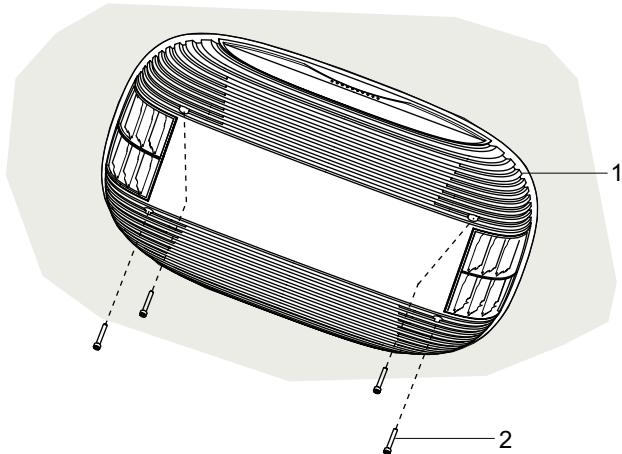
Fijación del conjunto de distribuidor de aire al soporte de montaje
